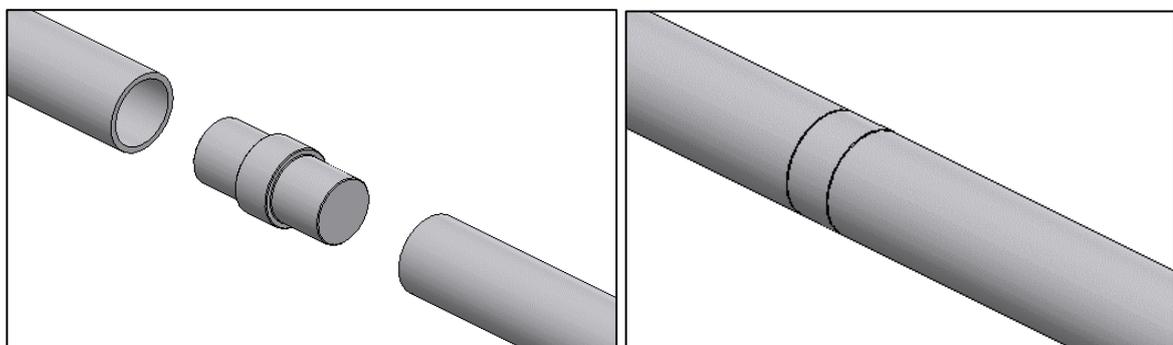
Instalación del manguito rígido entre barandales adyacentes.
